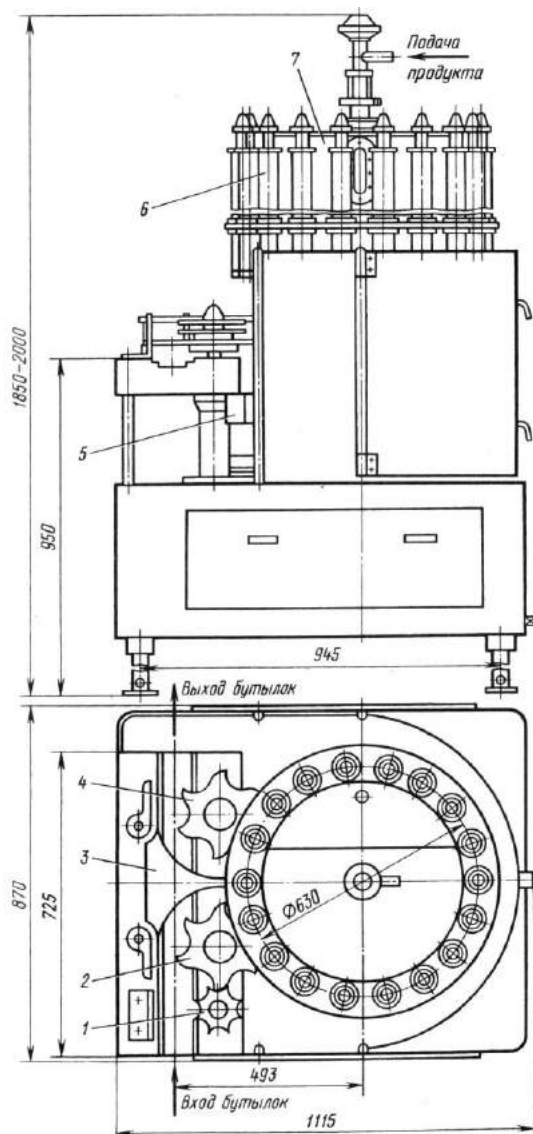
Роторный автомат для фасования напитков модели D9-BP2M-6: 1 – дилильная зірочка; 2 – допоміжний ротор для завантаження пляшок Д1; 3 – стіл; 4 – розванта-жувальний допоміжний ротор Д2; 5 – робочий ротор; 6 – фасувальний пристрій; 7 – витратний резервуар
